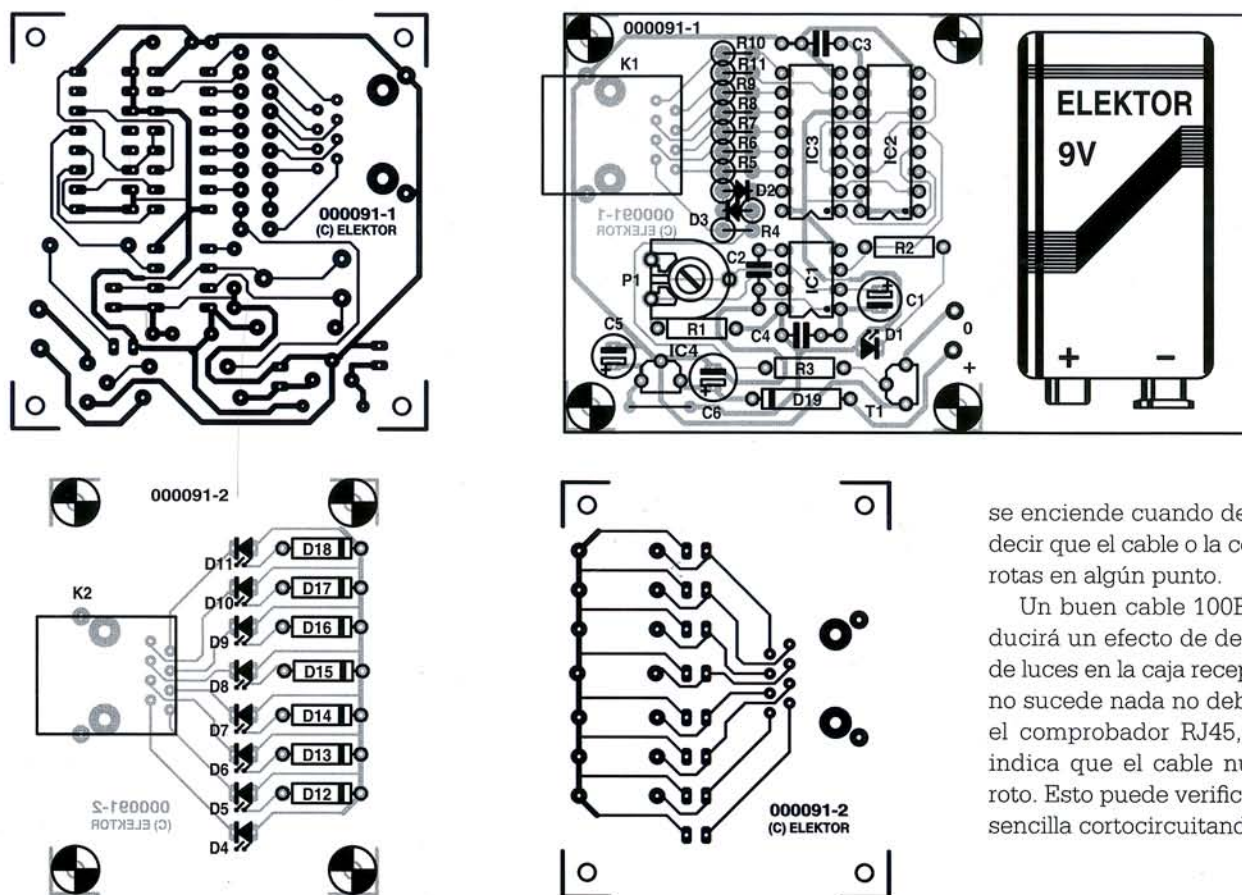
Diseño de PCB para el comprobador RJ45 (placas no disponibles en Servicio de Lectores).
